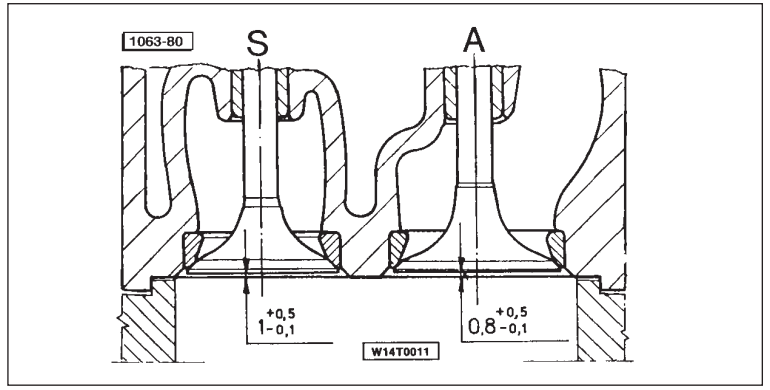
Retrait des soupapes par rapport au plan d'appui du joint de culasse moteur.
